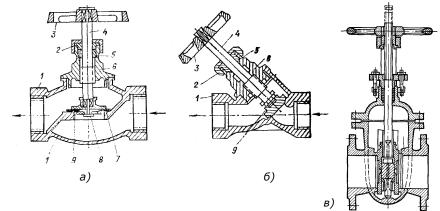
Запорная арматура: a — вентили прямой и косой; b) — задвижка проходная; 1 — корпус; 2 — накидная гайка; 3 — маховик; 4 — шпиндель; 5 — сальник; 6 — головка; 7 — резиновая прокладка; 8 — винт и шайба; 9 — клапан в сборе
